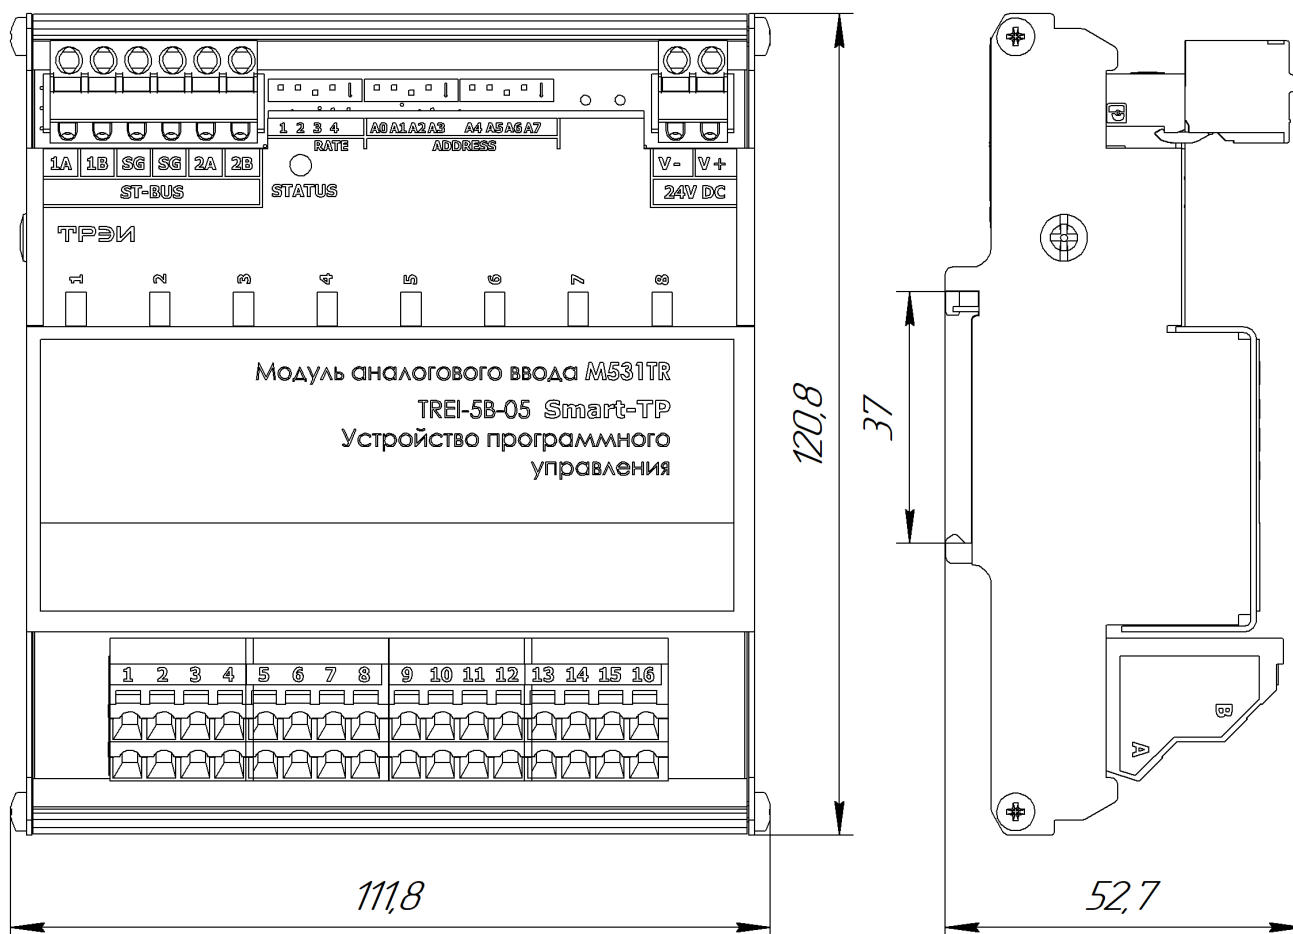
Чертеж общего вида M531TR с указанием габаритных и присоединительных размеров
